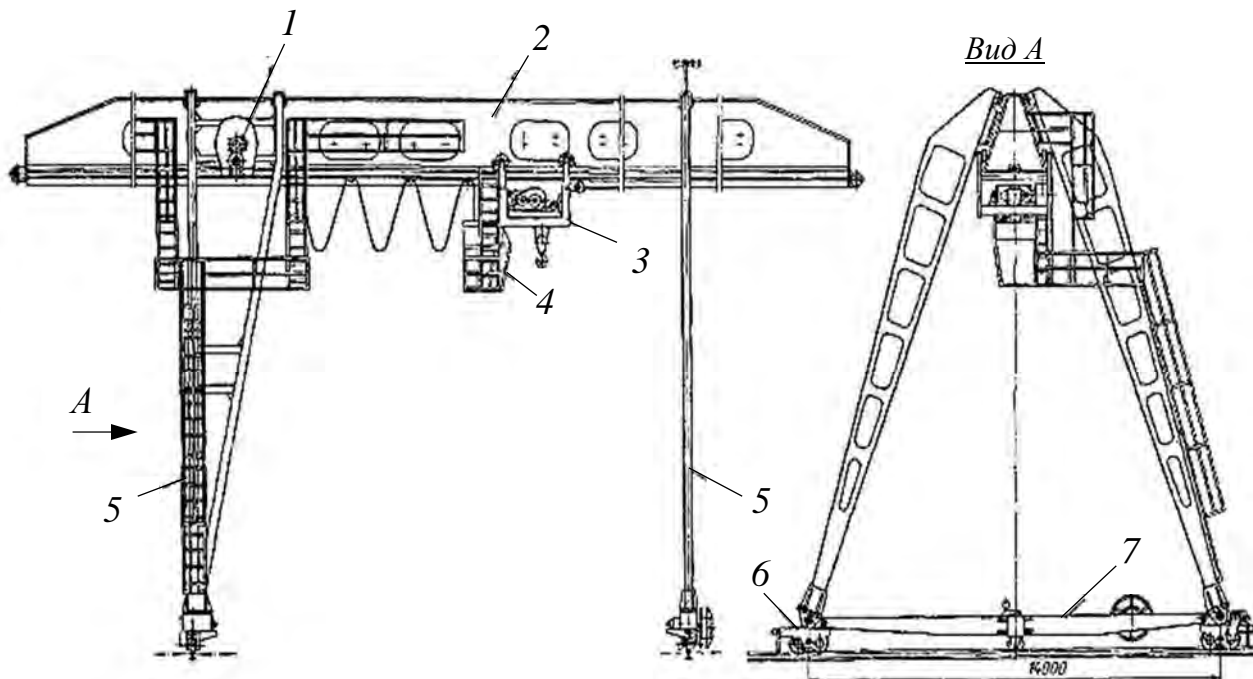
Самомонтирующийся козловой кран: 1 – механизм передвижения тележки; 2 – пролетное строение; 3 – грузовая тележка; 4 – подвижная кабина; 5 – опоры коробчатого сечения; 6 – ходовая тележка; 7 – стяжка опор
